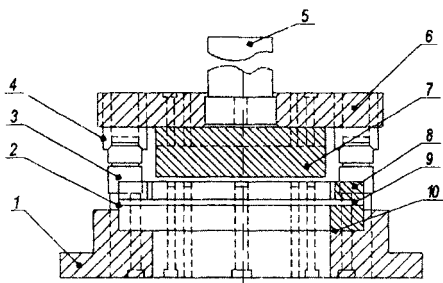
Штамп закрытого типа с направляющими колонками для вырубки из полосы
